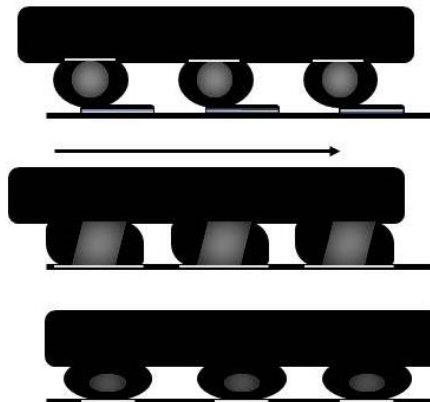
BGA auto-alineándose a la plataforma del PCB debido a la tensión superficial de la soldadura [2].
